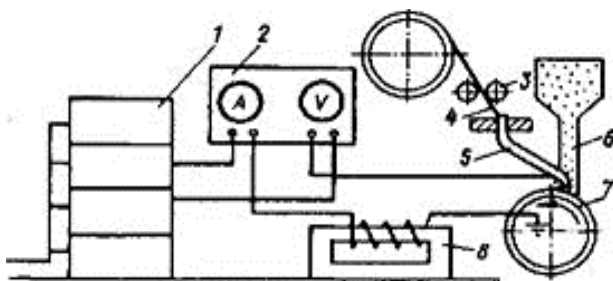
Схема установки для автоматической наплавки под слоем флюса:
